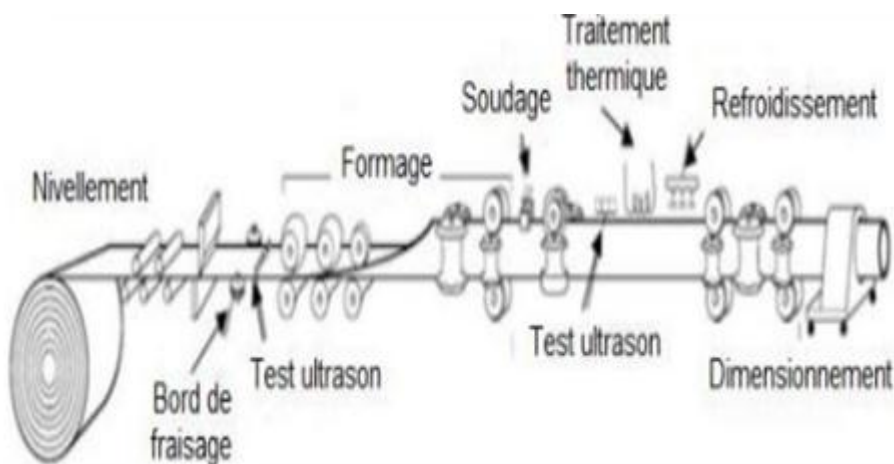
Technique de fabrication des tubes soudés en spirale
